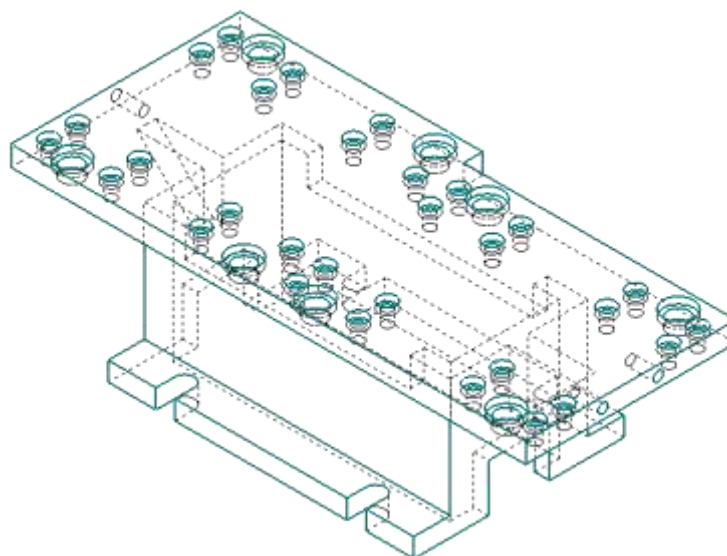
Загальний вигляд стола фрезерного приспособлення
